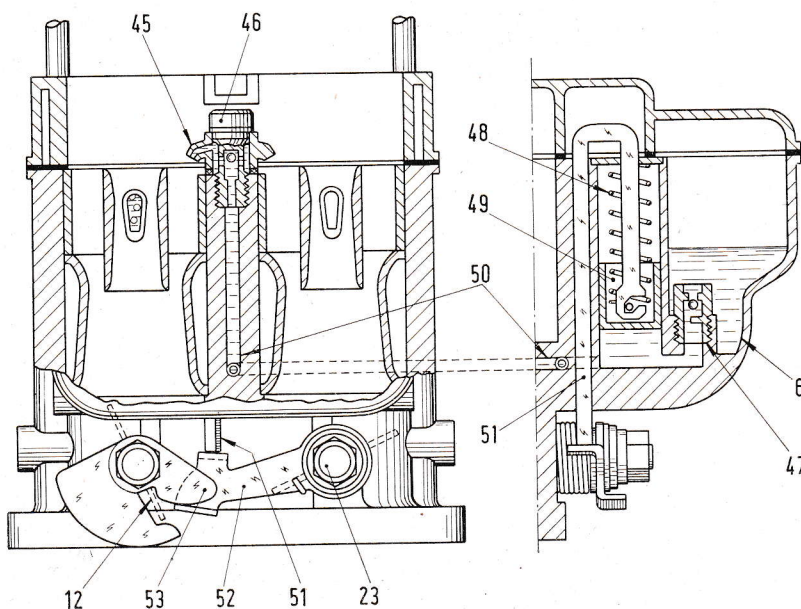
Betriebsschema, beim Gasgeben, des Weber-Vergasers 34 DCHD 4 (für Motor 115 C.005).
